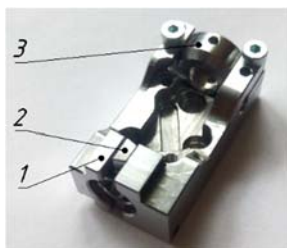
Внешний вид корпуса резонатора эрбиевого лазера
